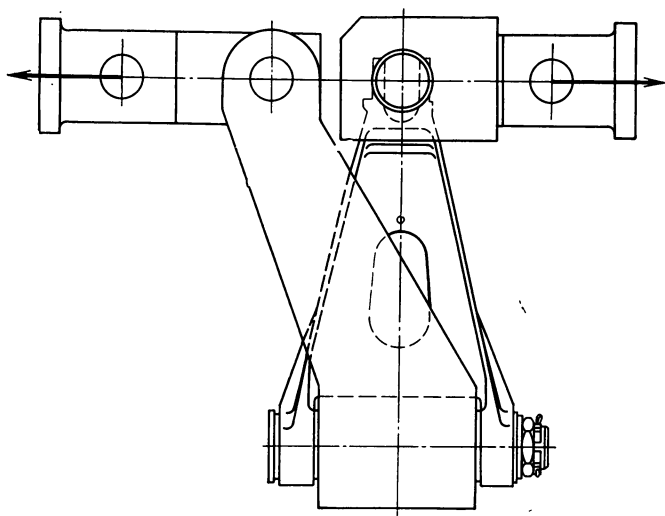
Схема специального приспособления для испытания нижнего звена шлиц-шарнира основной стойки шасси
